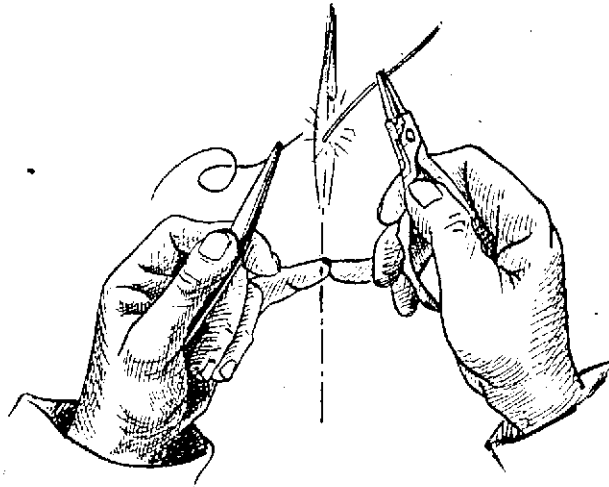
Soudure des fils de cuivre et de platine.
